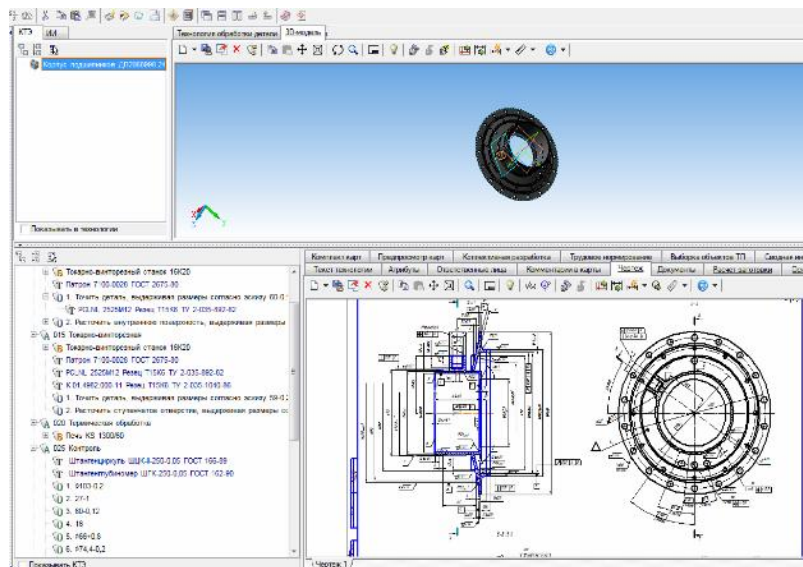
Ассоциативный чертеж и 3D модель детали «Корпус подшипника»
